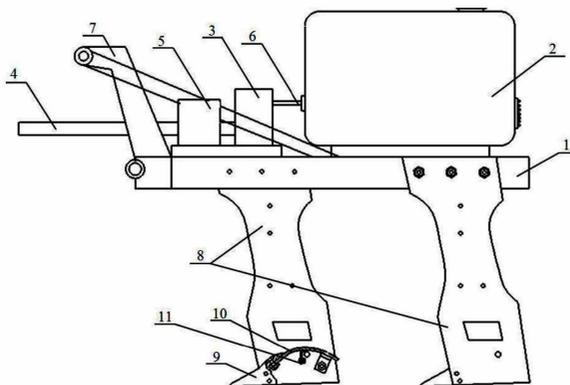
Схематическое изображение устройства для создания полосы противопожарного назначения: 1 – рама; 2 – резервуар для жидкости; 3 – редуктор; 4 – привод от вала отбора мощности; 5 – насос высокого давления; 6 – трубопровод; 7 – навеска; 8 – стойки; 9 – культиваторная лапа; 10 – сферический козырек; 11 – форсунка
